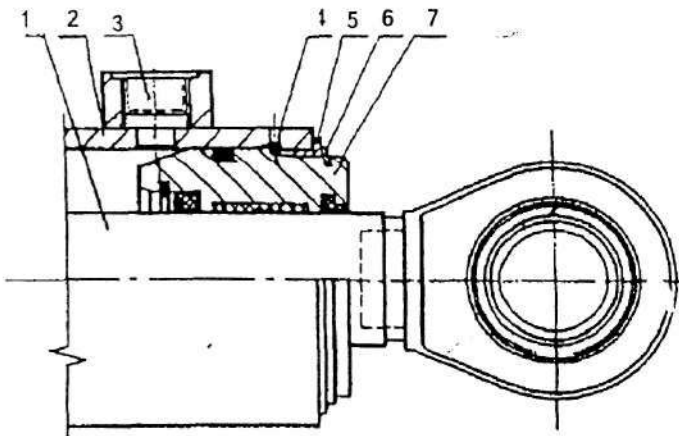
Схема передней втулки поршневого гидроцилиндра
